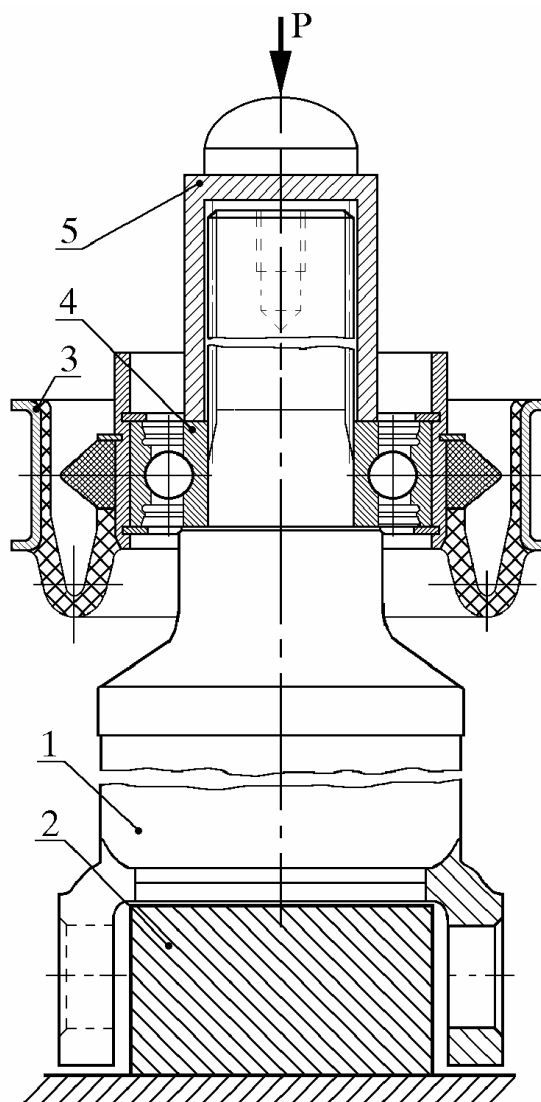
Напрессовка опоры в сборе на хвостовик промежуточного карданного вала:
